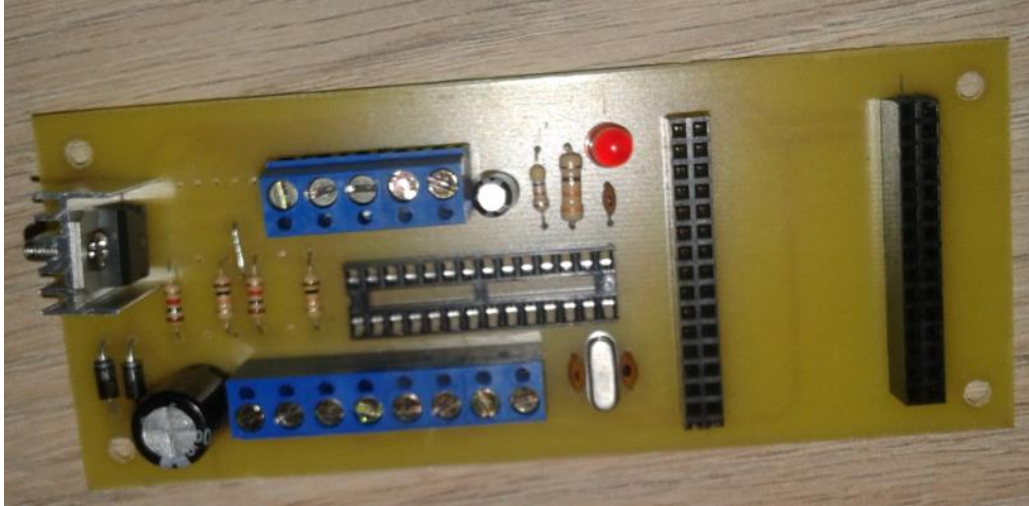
3. Placa de control con elementos soldados.
